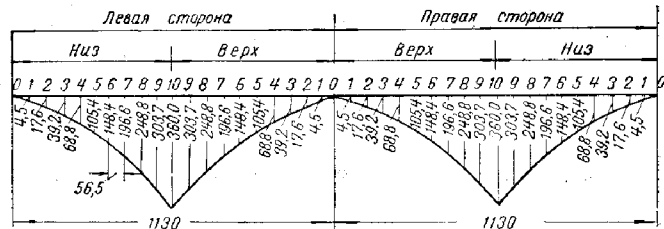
Развертка конца отрезка сварного тройника.
